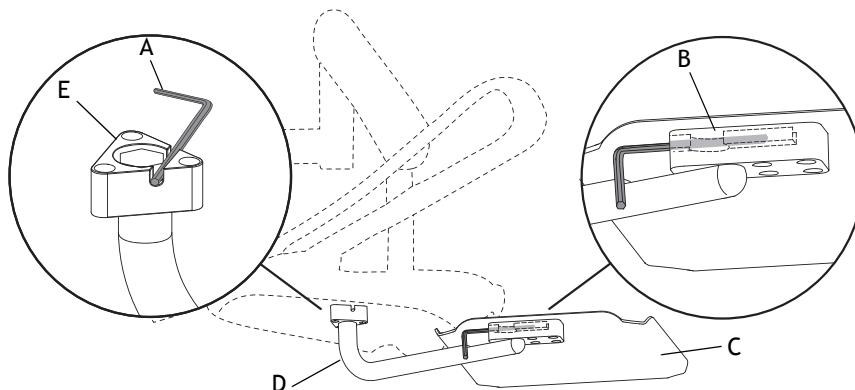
Регулировка поворота держателя лотка (традиционный модуль управления)
